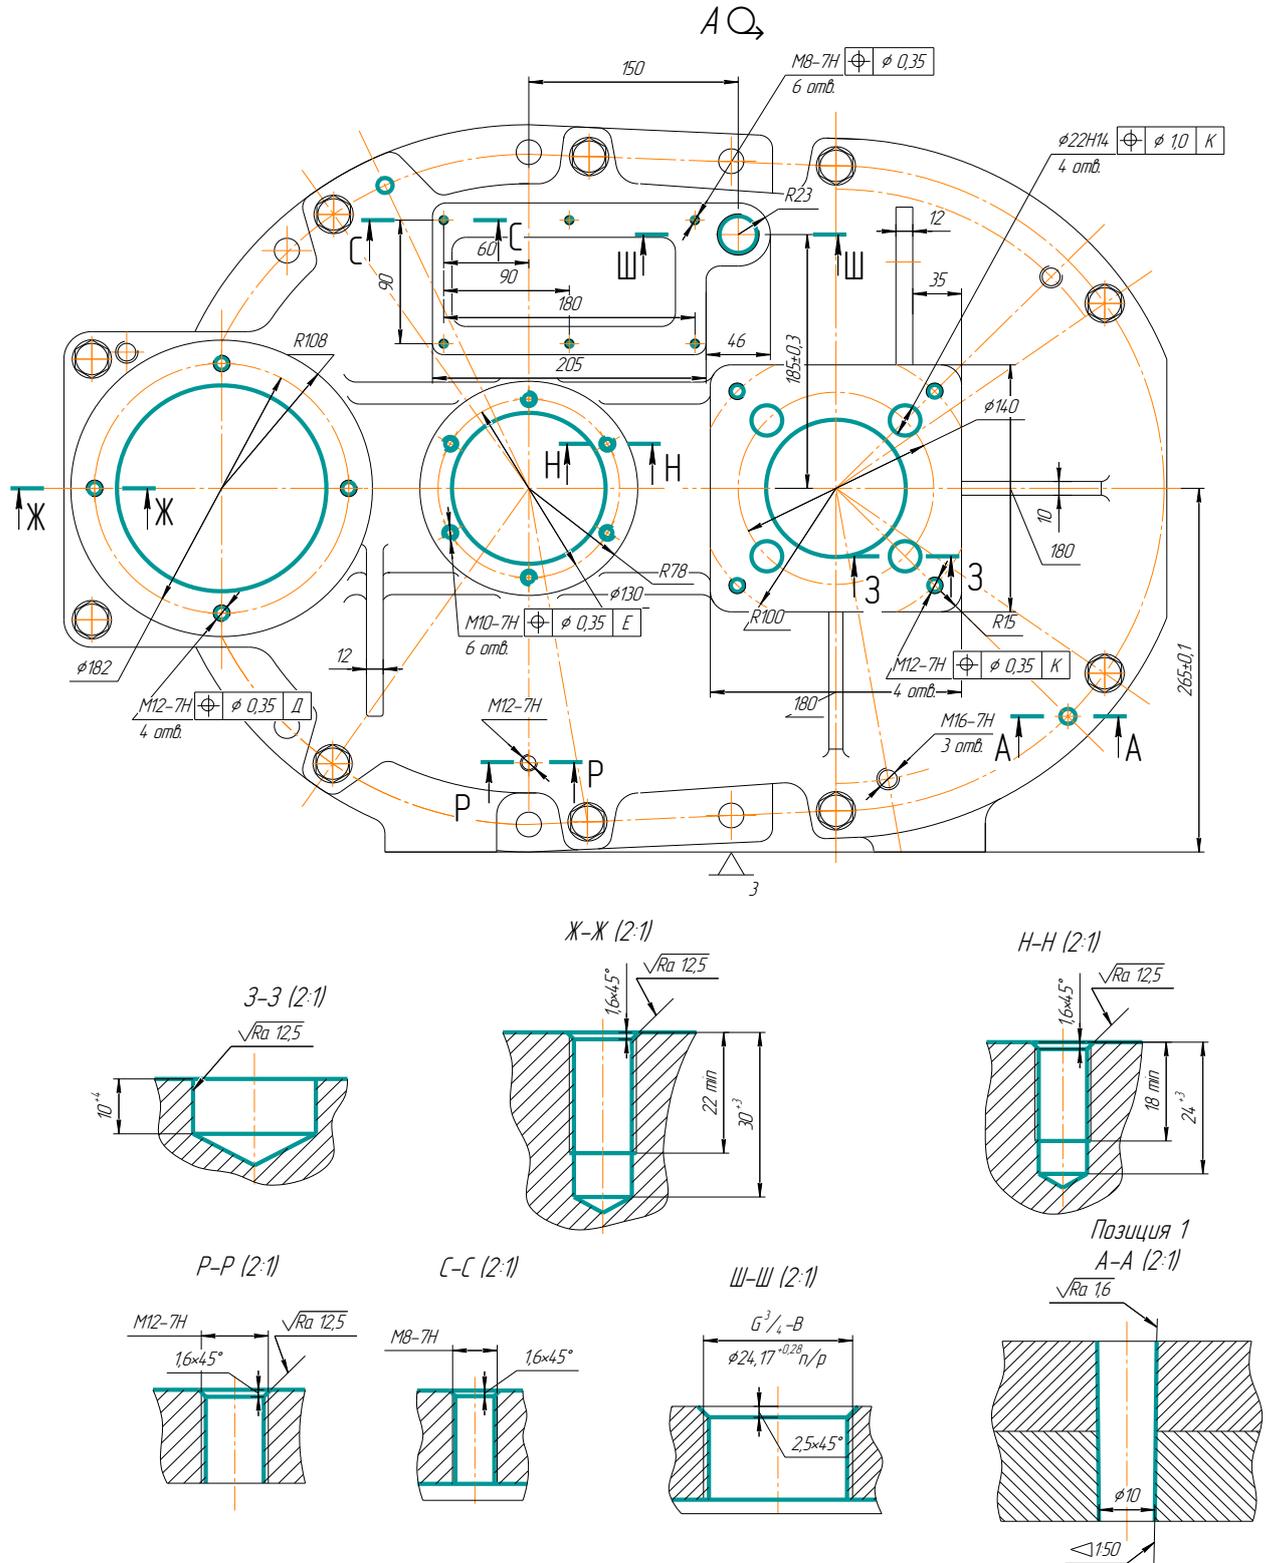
Схема базирования корпуса редуктора в сборе (Операция 020 Сверлильно-фрезерно-расточная)
